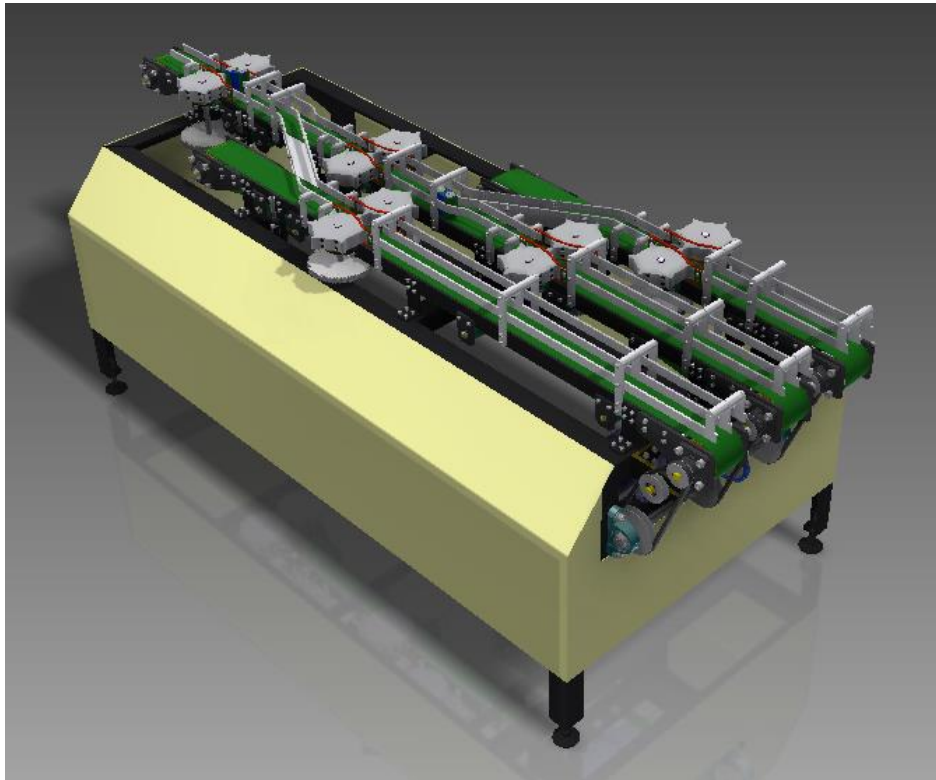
Vista en CAD de la máquina Ordenadora completa
